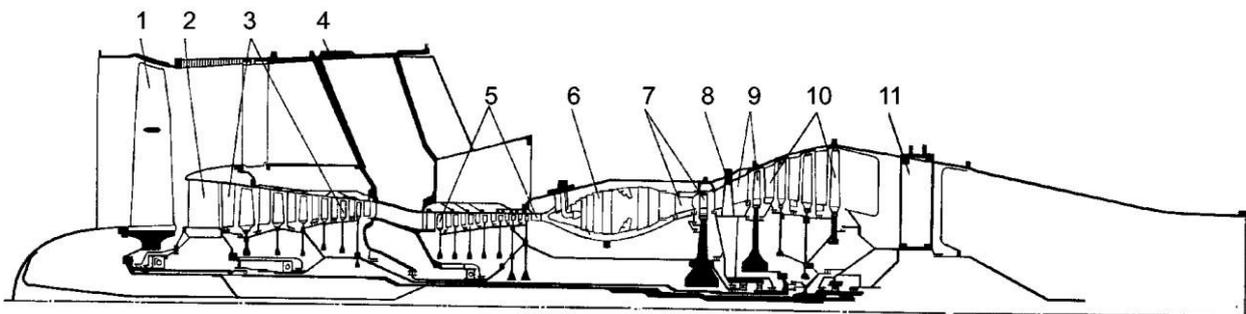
Конструктивная схема трехвального ДТРД:
